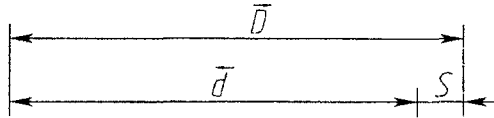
Размерная цепь для сборочного узла двигателя автомобиля
